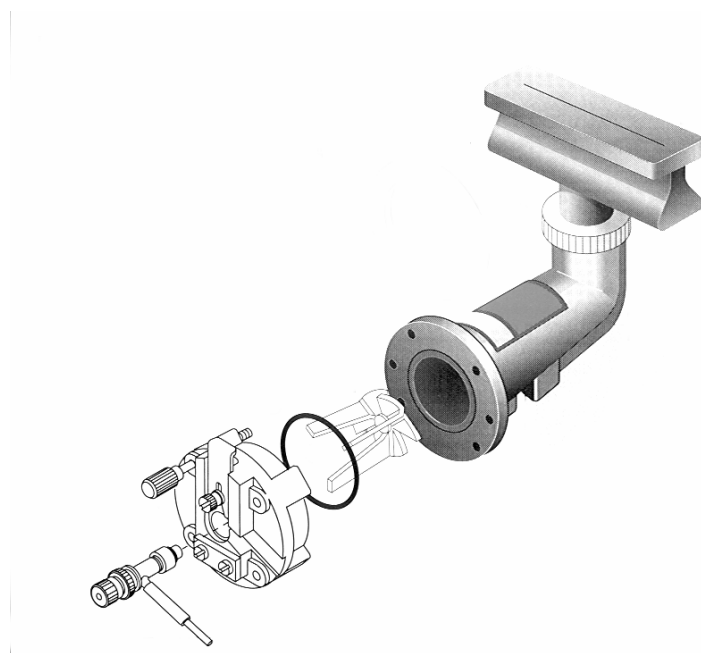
Vista explodida de um conjunto nebulizador/queimador (cortesia Perkin Elmer)
